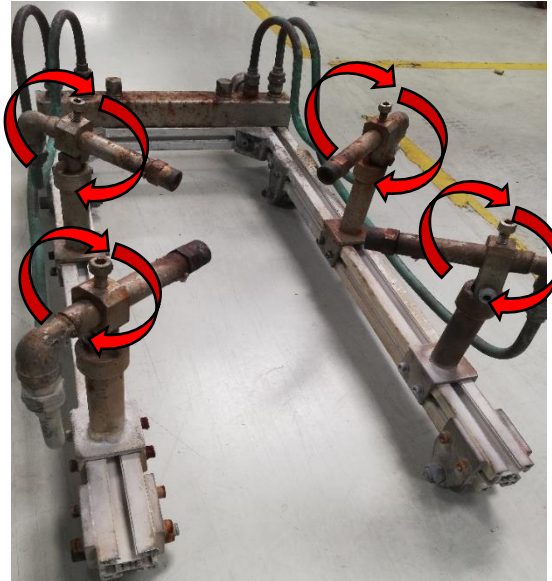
Carros de soldadura (Empresa em estudo).
